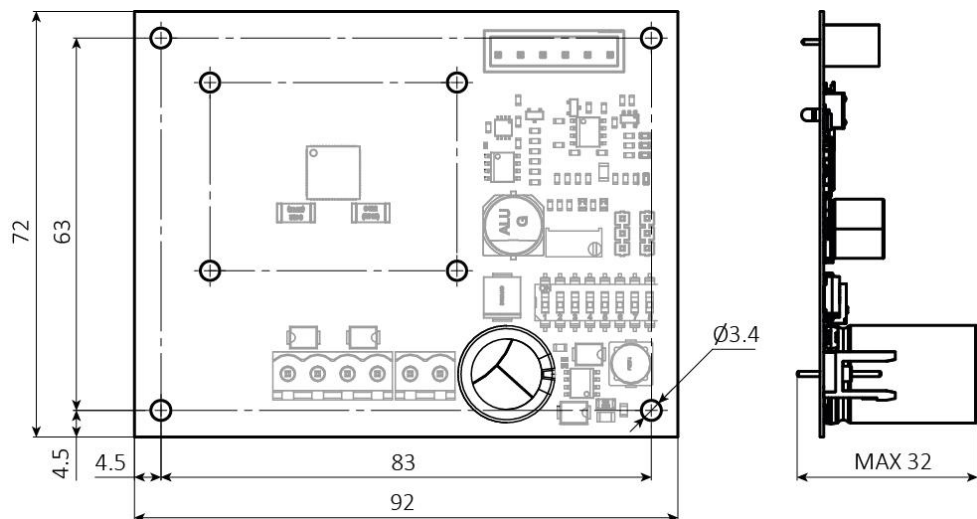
Габаритные и присоединительные размеры драйвера шагового двигателя SMD-1.6.
